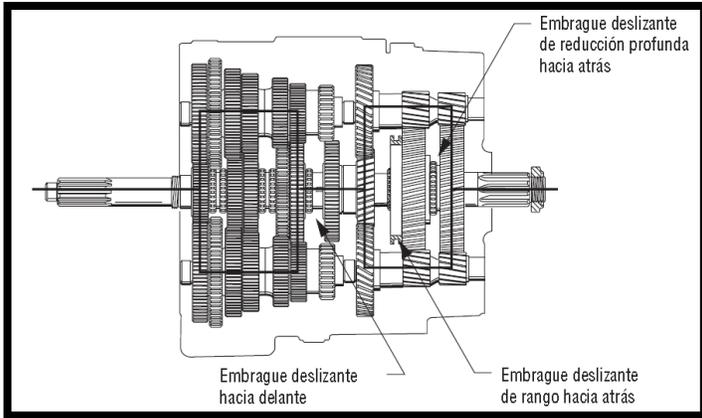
Reducción profunda 1 (DR1), transmisión tráiler: Fuente [34]
